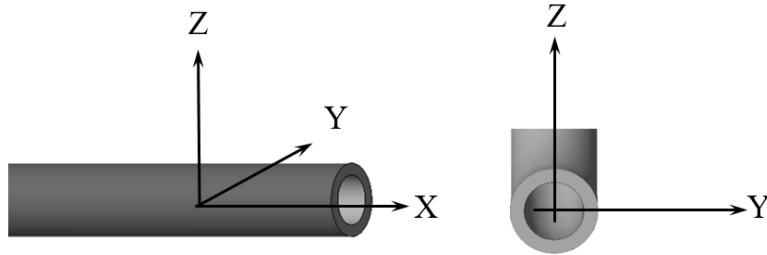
Eje longitudinal ("X") de la resistencia, y vista de la sección transversal.
